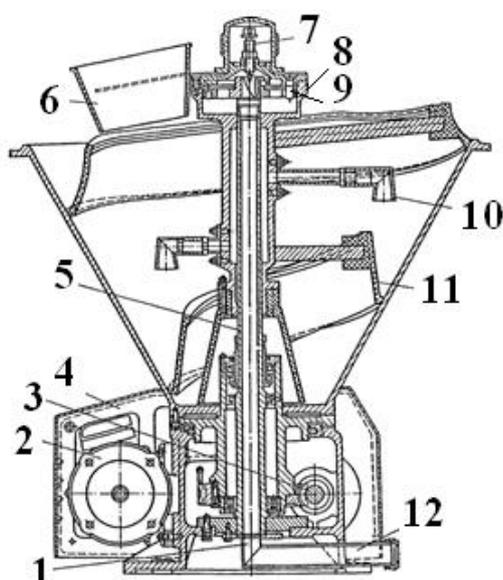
Тестоокруглитель Т1-ХТН с конической несущей поверхностью и внутренней формующей спиралью
